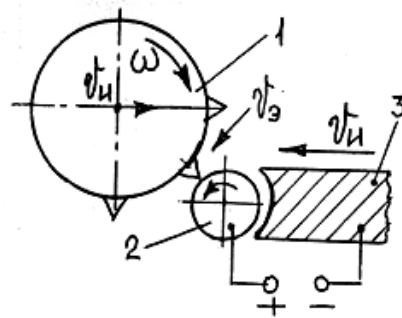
Схема анодно-абразивного шліфування електронейтральним інструментом: 1 – абразивний круг; 2 – заготовка; 3 – електроінструмент
